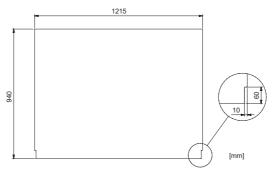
Dimensions de la planche latérale pour gravier. Remarque : des encoches sont pratiquées dans les deux angles inférieurs de la planche.
